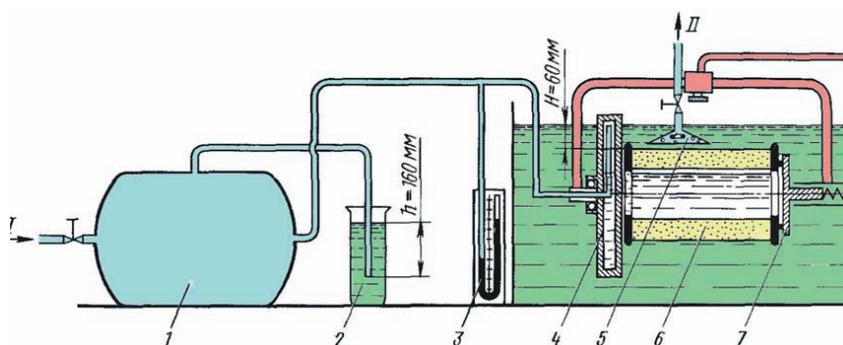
Схема установки для проверки фильтрующего элемента опрессовкой сжатым воздухом в воде: 1 — воздушный баллон; 2 — жидкостный клапан; 3 — контрольный манометр; 4 — полая крышка; 5 — прозрачный колпак; 6 — фильтрующий элемент; 7 — поджимная крышка; I — подвод сжатого воздуха; II — в атмосферу.
